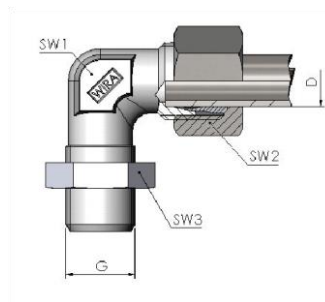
= Einschraubzapfen Form A DIN 3852 (Dichtfläche, ohne Bund)
